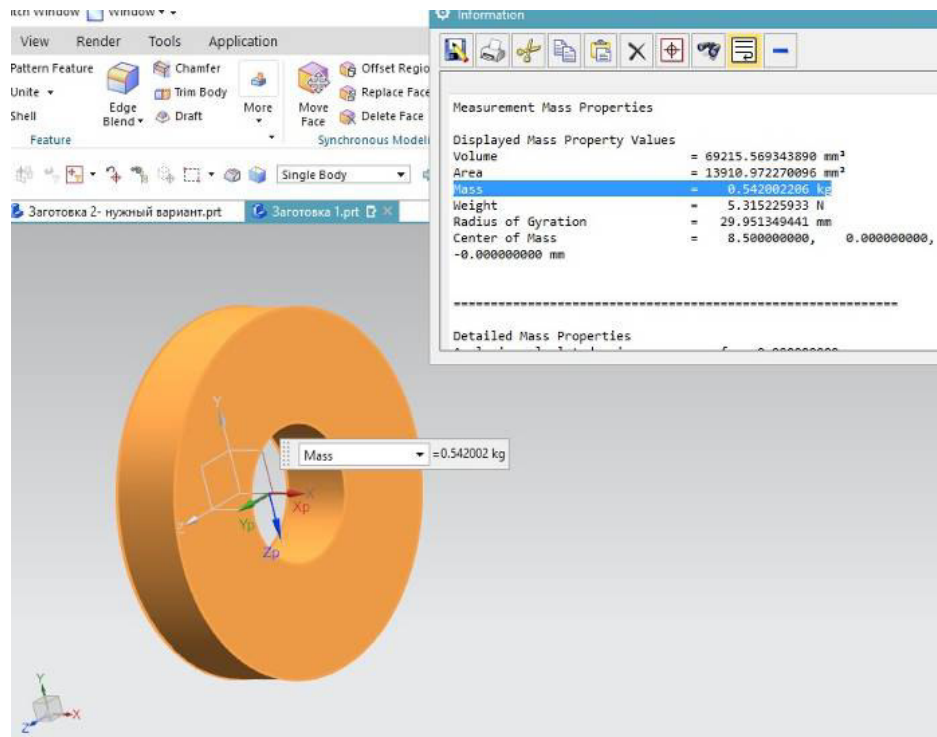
Модель відлітої в піщані форми заготовки
